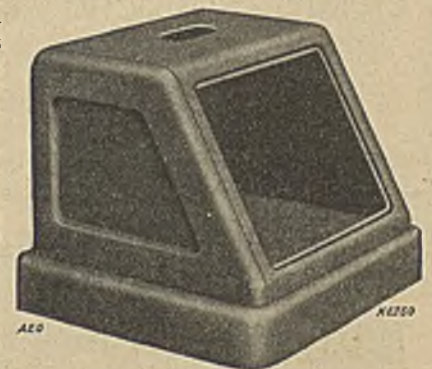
Punktweise geschweißtes Telephongehäuse.
